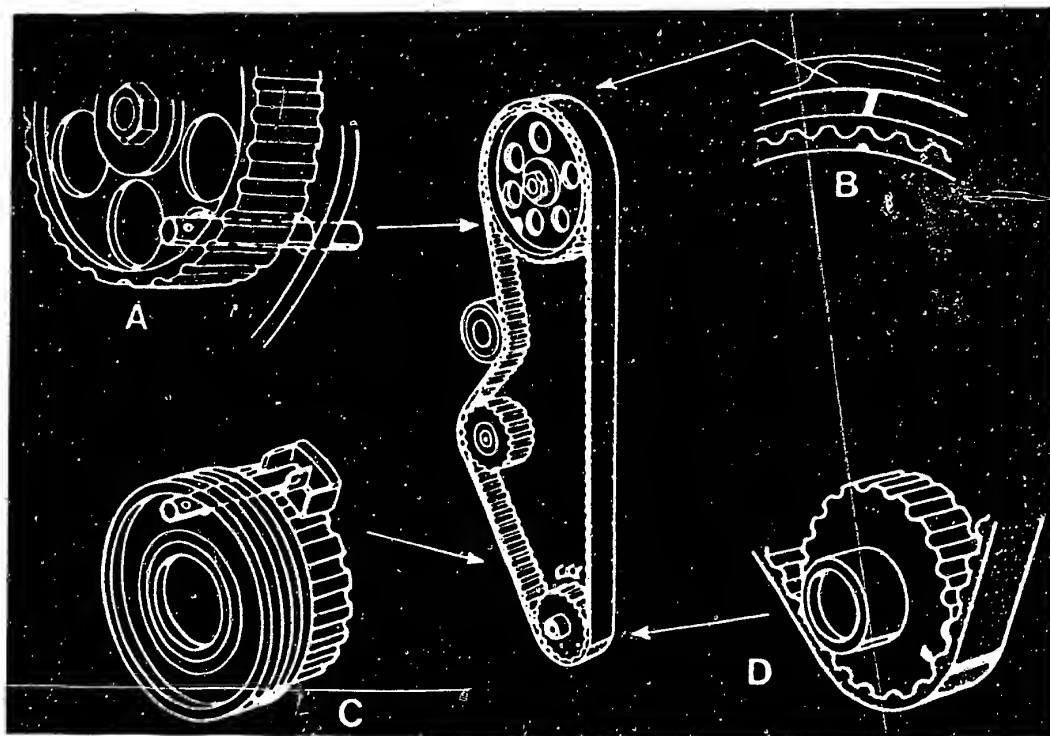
Ausrichtung der Steuerräder. A und B zeigen die Position des Nockenwellenrades. C und D diejenige des Keilriemen- und Kurbelwellenrades.
